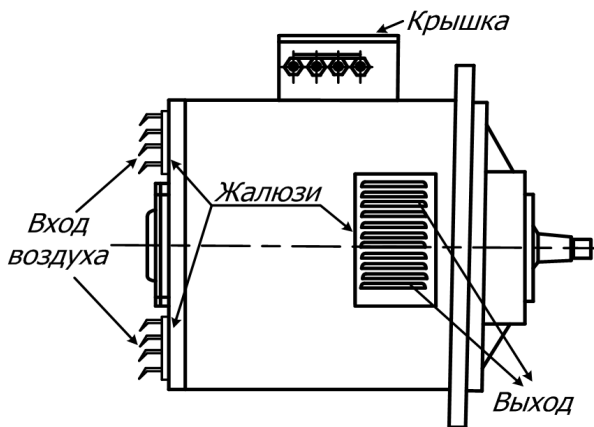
Предлагаемый вариант размещения вентиляционных отверстий тягового двигателя типа ДТН-45
